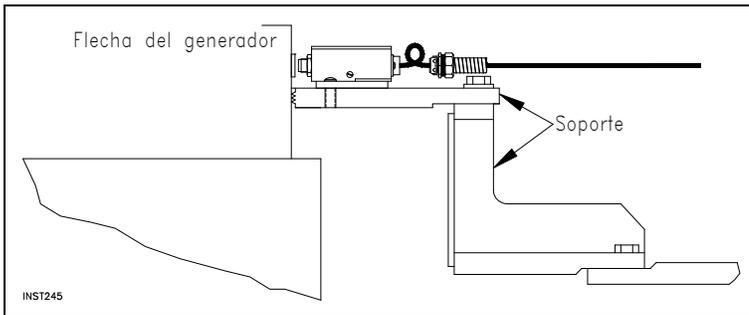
Dibujo de una ménsula de montaje de dos piezas
